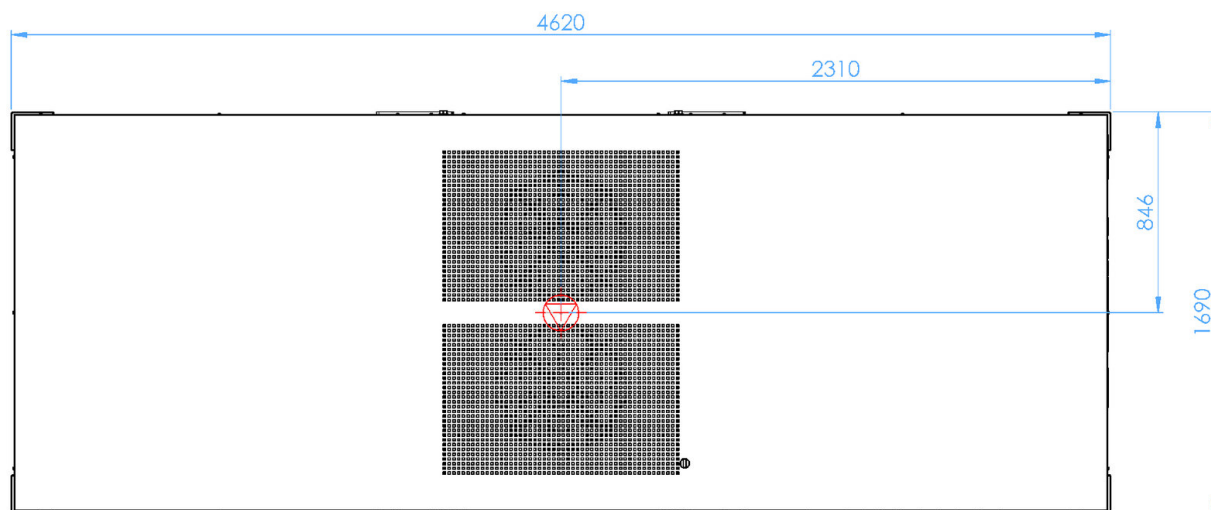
Draufsicht mit Bemaßung und Lage des Schwerpunkts [in mm]
